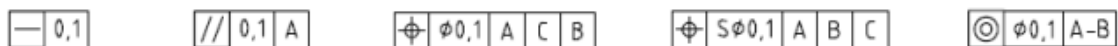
Indicadores de tolerancias geométricas. Copyright ISO 1101:2012
